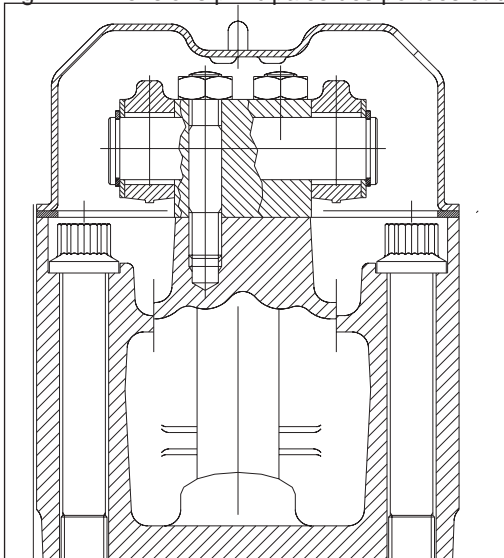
Vue en coupe de l'ensemble support-culbuteurs.
